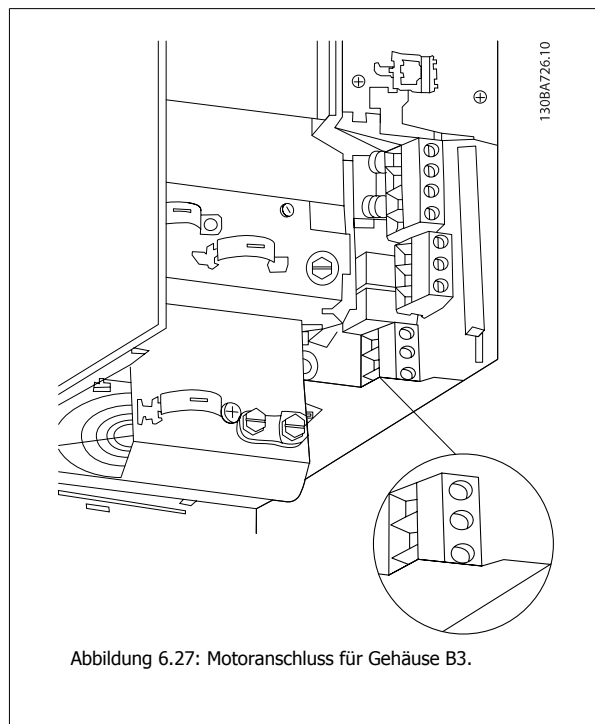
Motoranschluss für Gehäuse B3.
